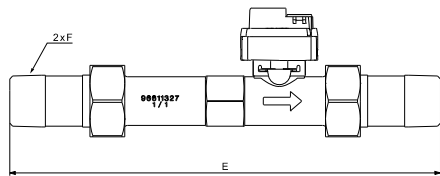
Abmessungen des Sensors MFS 10-100 l/min (mit Adaptern)
